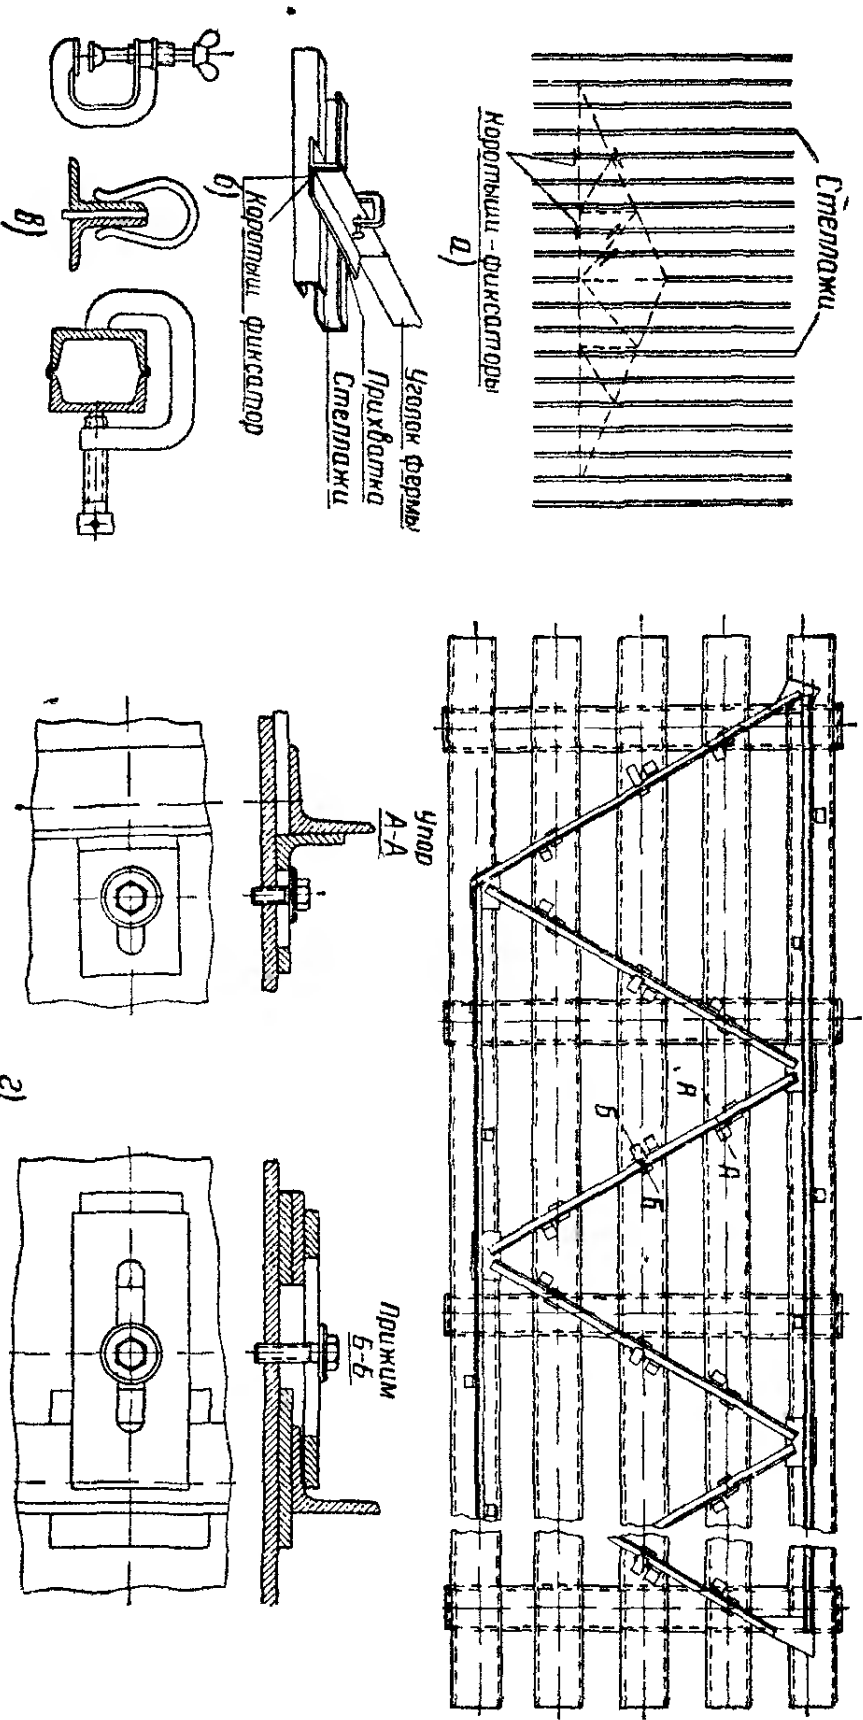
Приспособления для сборки и сварки решетчатых стропильных ферм:
